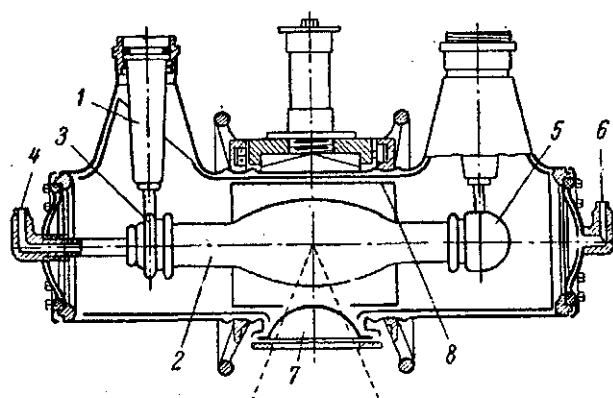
Защитный кожух для трубки ЗБПМ-200 с проточным масляным охлаждением.
